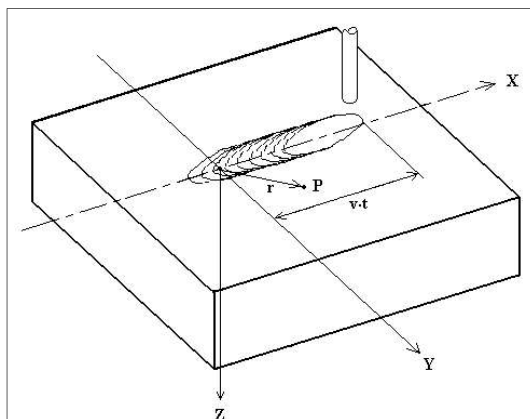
Soldagem sendo realizada sobre a superfície de um corpo e ponto (P) no seu interior.
